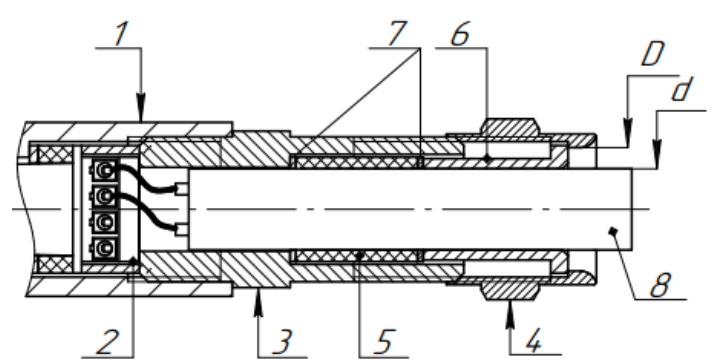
Габаритные и установочные размеры задающего блока Ex IO 102
